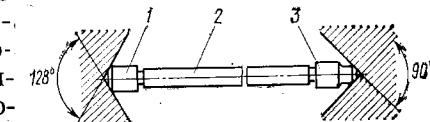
Схема проверки прямолинейности толкающей штанги в конусных оправках:
